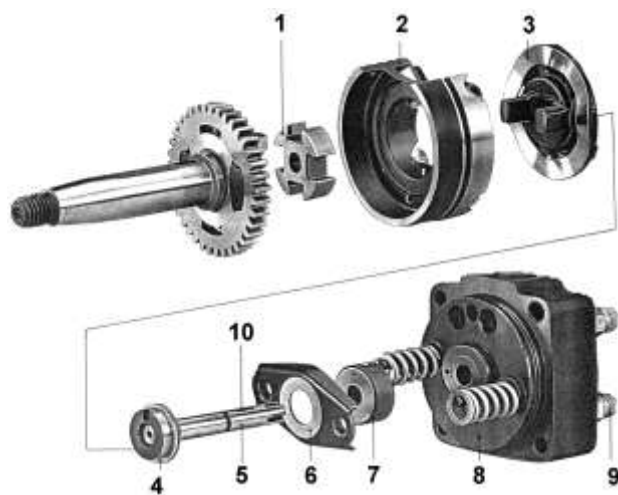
Детали насосной секции ТНВД VE: 1 - муфта; 2 - обойма с роликами; 3 - кулачковая шайба; 4 - хвостовик; 5 - плунжер; 6 - планка; 7 - дозирующая муфта; 8 - пружина; 9 - штуцер; 10 - выфрезеровка-распределитель.
